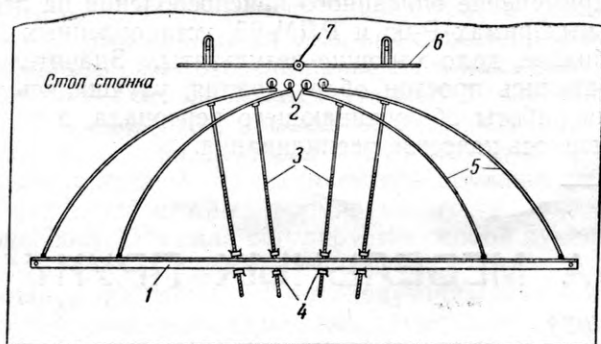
Прижимное устройство для одношпиндельного фрезерного станка:
